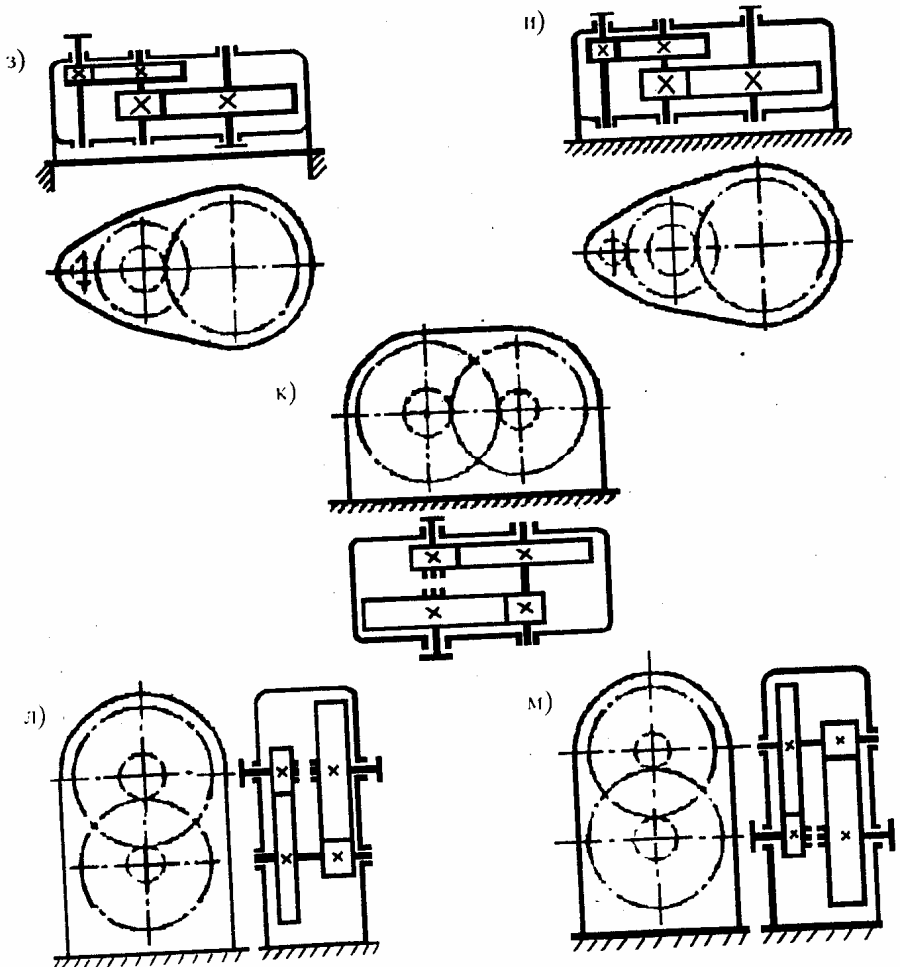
(продолжение) Кинематические схемы цилиндрических двухступенчатых редукторов (Ц2)
